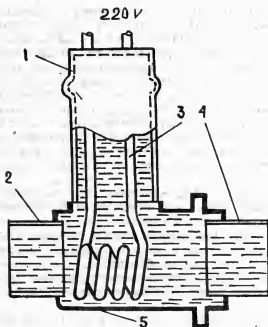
Электрический подогреватель: 1 — выходной патрубок; 2 — патрубок перепускного шланга; 3 — электронагреватель; 4 — входной патрубок; 5 — корпус термостата.
